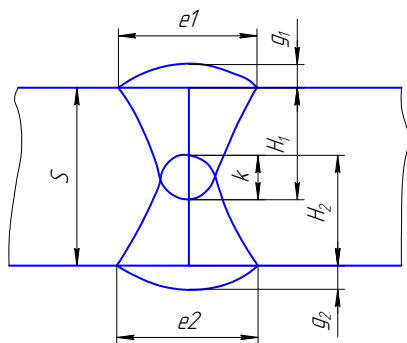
Условия обеспечения полного провара при сварке стыковых соединений
